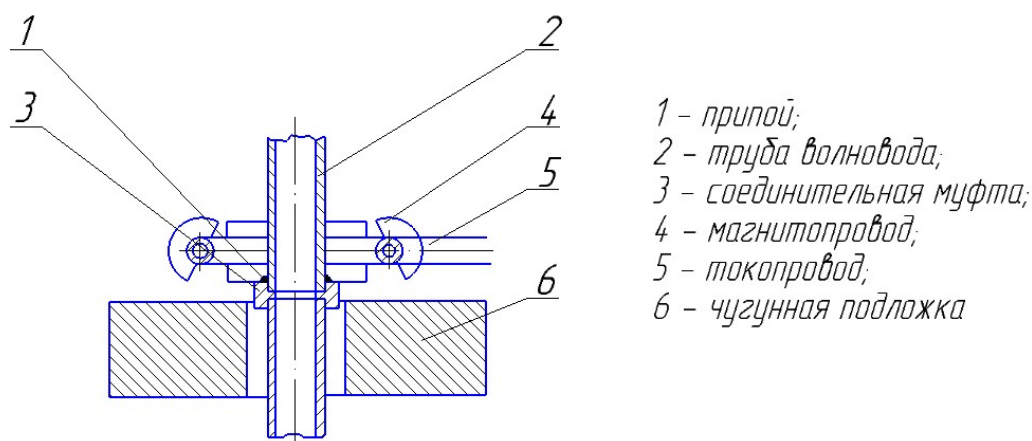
Общий вид устройства для пайки соединительной муфты и трубы волновода
